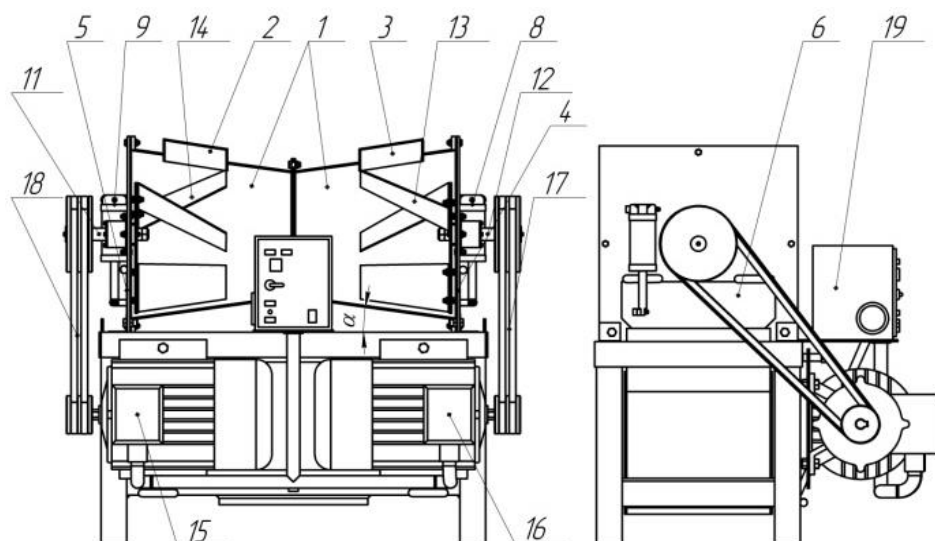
Схема смесителя новой конструкции: 1 – корпус; 2, 3 – загрузочный патрубков; 4, 5 – разгрузочные отверстия; 6, 7 – заслонки, 8, 9 – пневмоцилиндры; 10 – фланцы корпуса; 11, 12 – валы; 13, 14 – роторы с лопастями; 15, 16 – электродвигатели; 17, 18 – ременные передачи, 19 – пульт управления
